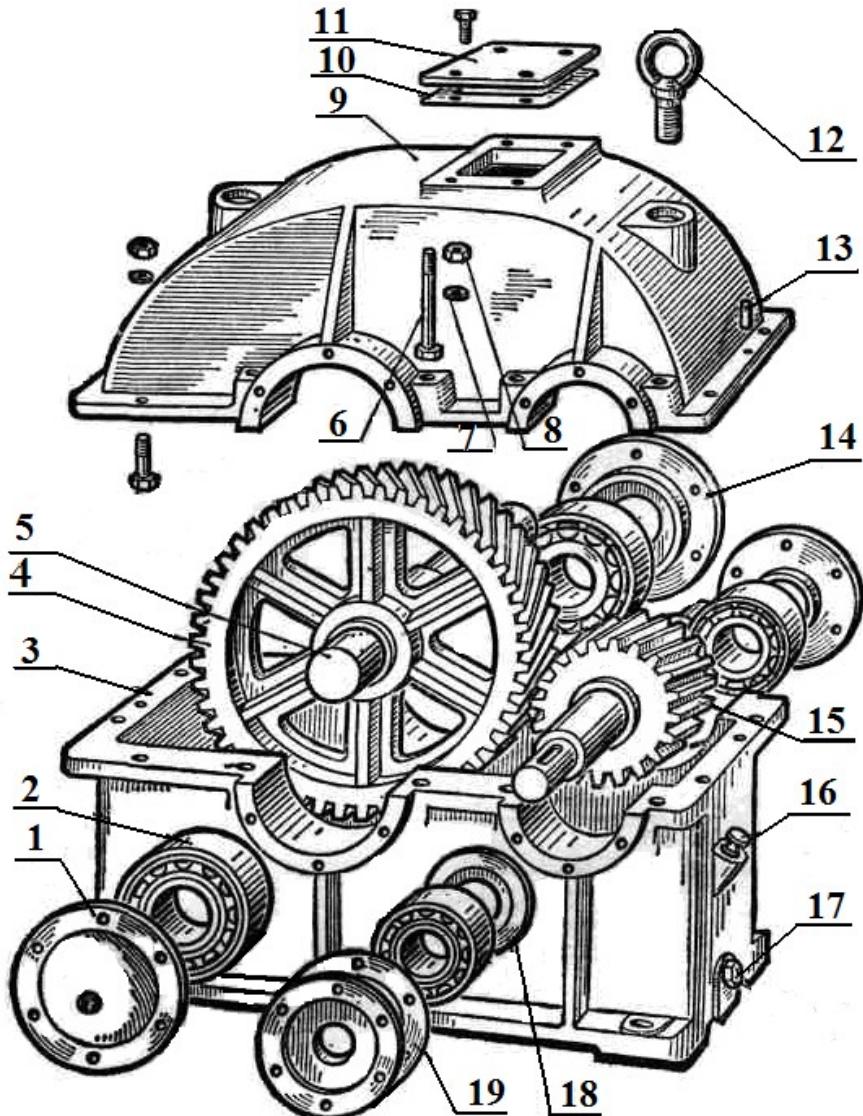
Редуктор цилиндрический в сборе: 1 – привертная крышка; 2 - подшипник; 3 – корпус редуктора; 4 – зубчатое колесо; 5 – ведомый вал; 6, 7, 8 – болт, шайба, гайка; 9 – крышка редуктора; 10, 11 – прокладка, крышка смотрового окна; 12 – рым болт; 13 – штифт; 15 – вал-шестерня; 16 – маслоуказатель; 17 – сливная пробка; 18, 19 – распорные кольца
